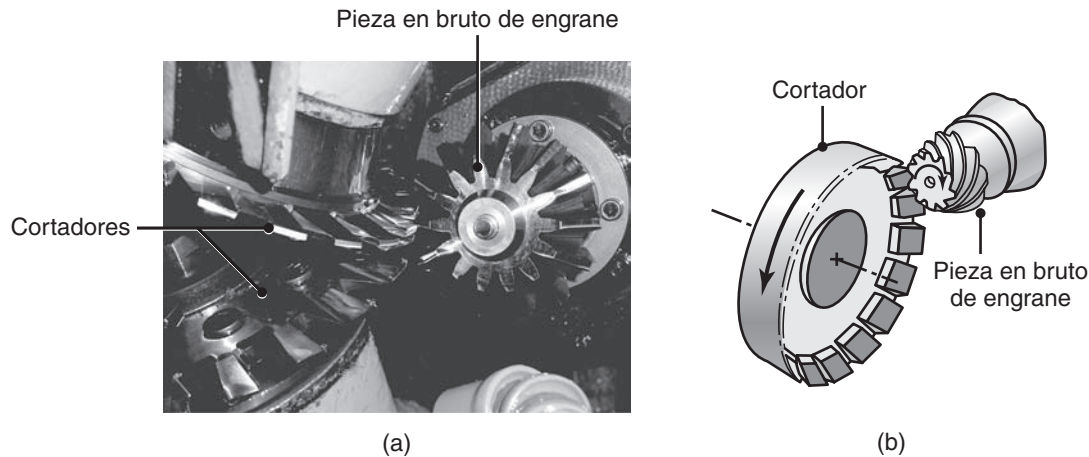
(a) Corte de una pieza en bruto de engrane cónico recto con dos cortadores. (b) Corte de engrane cónico helicoidal. *Fuente:* Cortesía de Schafer Gear Works, Inc.
